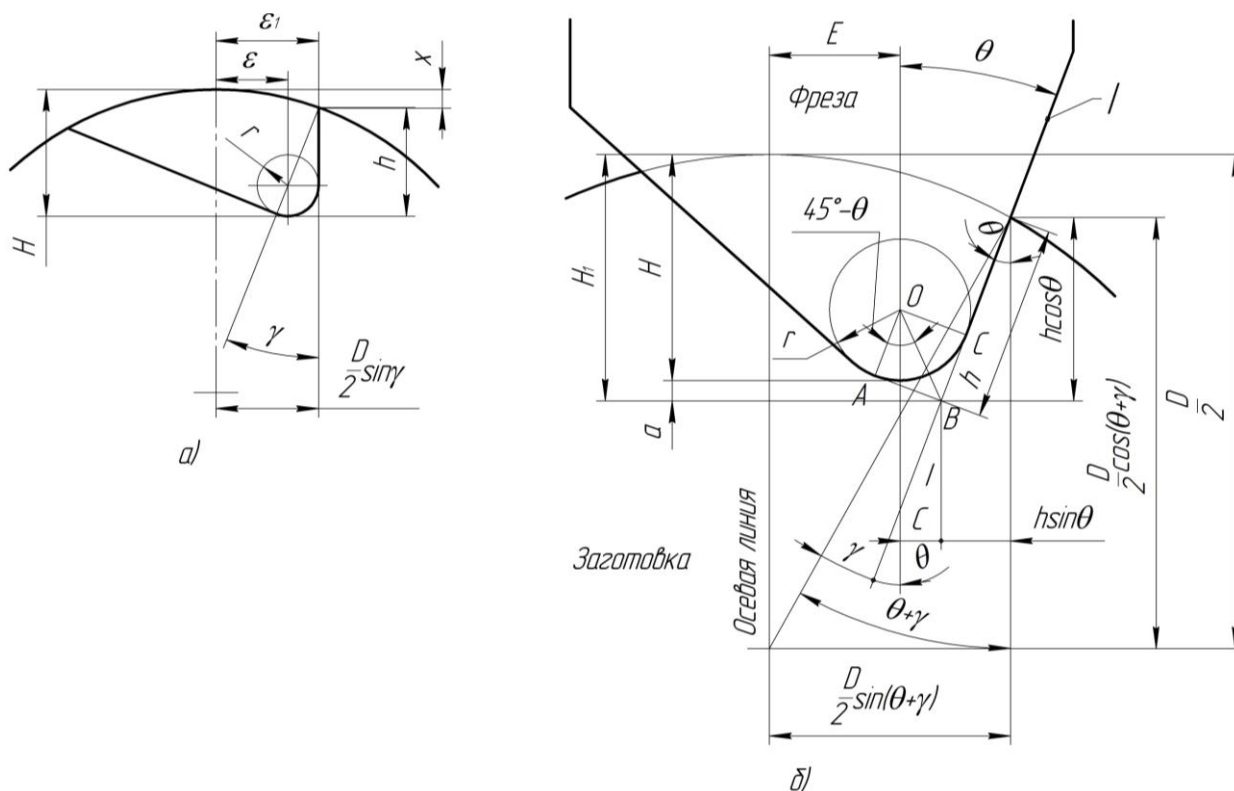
Схемы: *a* — расчета при фрезеровании прямых зубьев одноугловой фрезой; *б* — фрезерования прямых зубьев двухугловой фрезой
